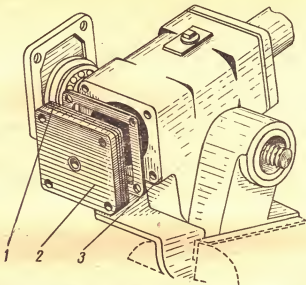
Регулировка осевого зазора в подшипниках рулевого механизма автомобиля УАЗ-69:
